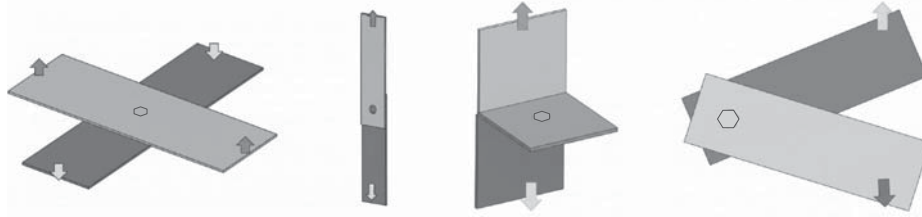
Испытания на механические свойства сварного соединения для определения параметров разрушения
